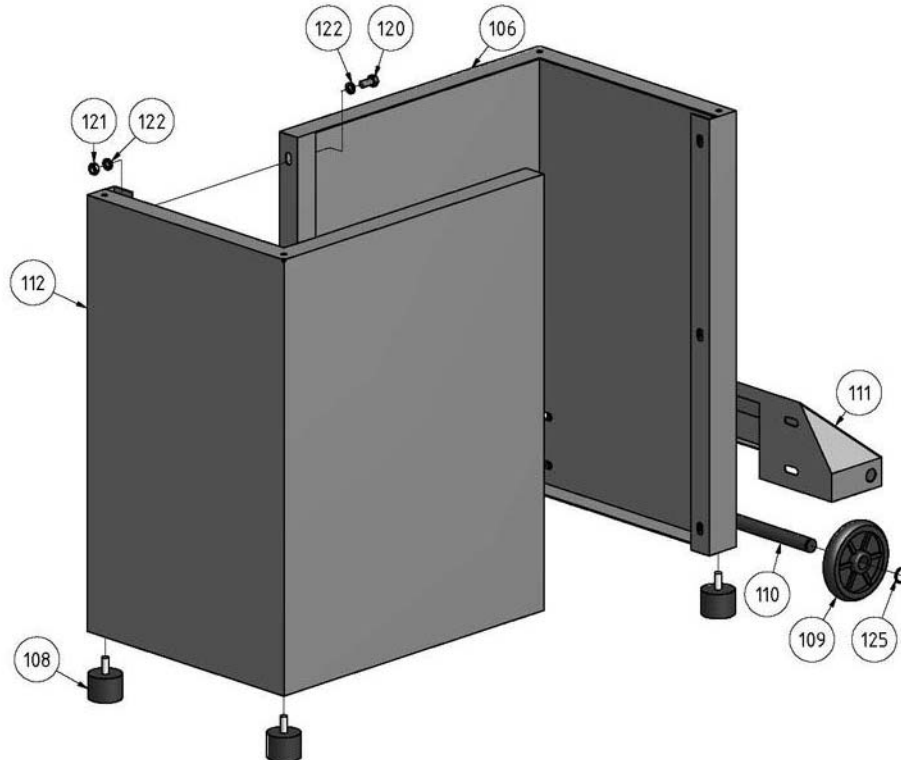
Ersatzteilzeichnung 4 von 4 - Parts drawing 4 of 4
